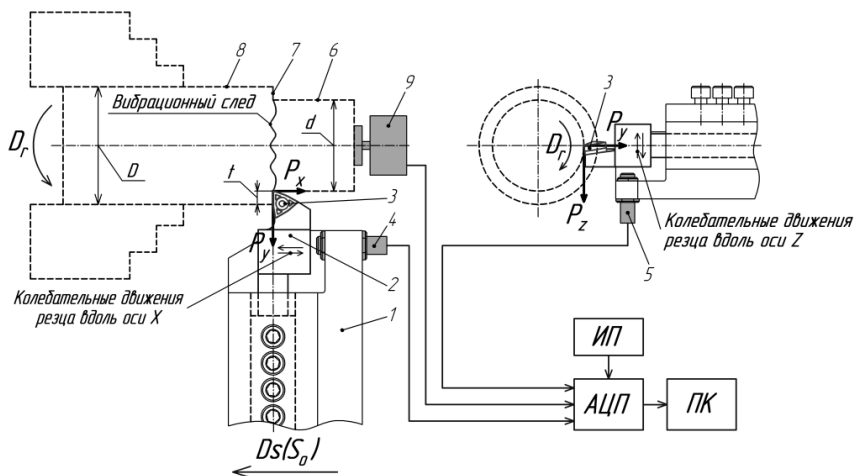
Схема экспериментального стенда измерения колебаний резца при точении: 1 – корпус устройства; 2 – упругий элемент; 3 – режущая пластина; 4 – датчик горизонтальных перемещений резца; 5 – датчик вертикальных перемещений резца; 6 – обработанная поверхность; 7 – поверхность резания; 8 – обрабатываемая поверхность; 9 – энкодер;  $D_r$  – главное движение резания;  $Ds(S_0)$  – движение подачи; АЦП – аналого-цифровой преобразователь; ПК – персональный компьютер; ИП – источник питания
